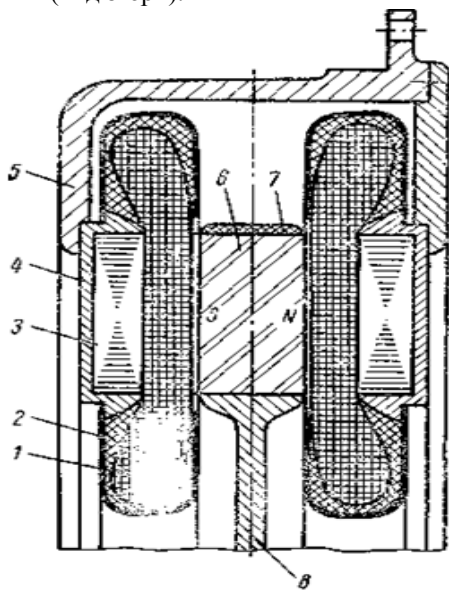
Моментний двигун з обмеженим кутом повороту ротора: 1 – обмотка; 2 – захисний кожух; 3 – ярмо статора; 4 – кільцевий стакан; 5 – корпус; 6 – постійний магніт; 7 – бандаж із склострічки; 8 – корпус ротора
